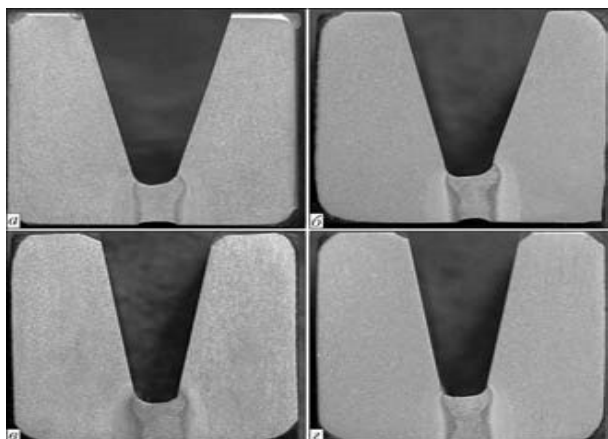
Макрошліфи кореневого шва, виконаного лазерним зварюванням з V-(а, б) та U-подібною (в, г) обробкою та притупленням 5 мм
